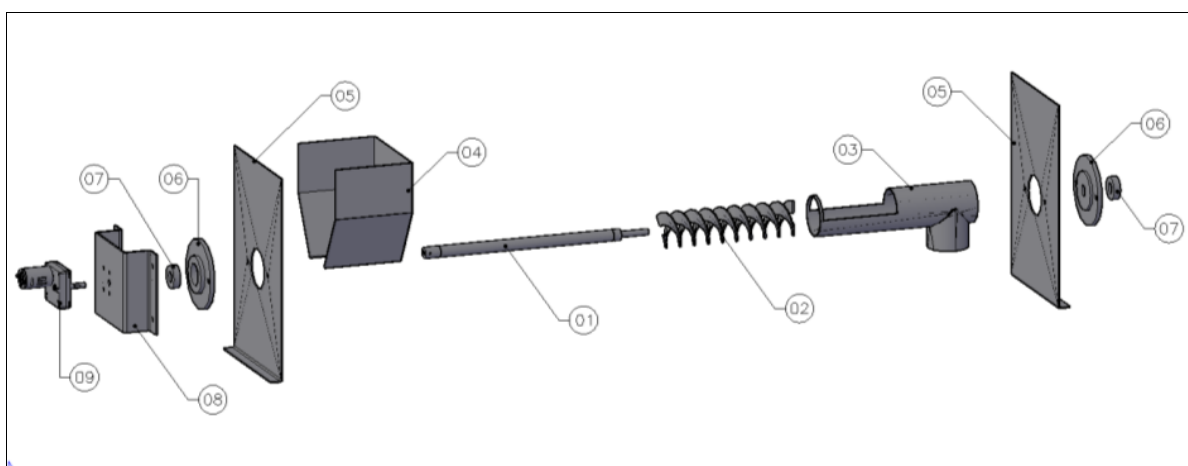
Modelagem do protótipo em CAD 3D “explodido”
